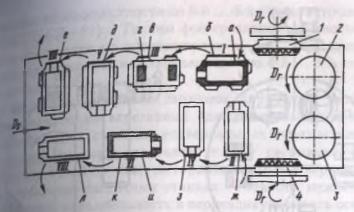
Схема обработки плоских поверхностей с перекладыванием заготовок и в два потока: 1-4-торцевые фрезы; I, III, V, VII - позиции обработки заготовки корпуса; II, IV, VI, VIII - позиции обработки заготовки крышки корпуса; а... л - обрабатываемые поверхности
